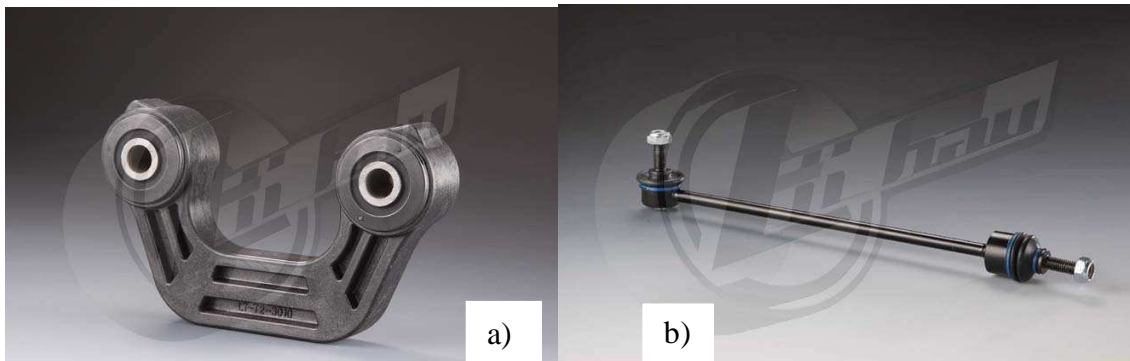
a) Conexión con dos bujes y barra de plástico; b) conexión con rotulas y ángulo entre ellas
